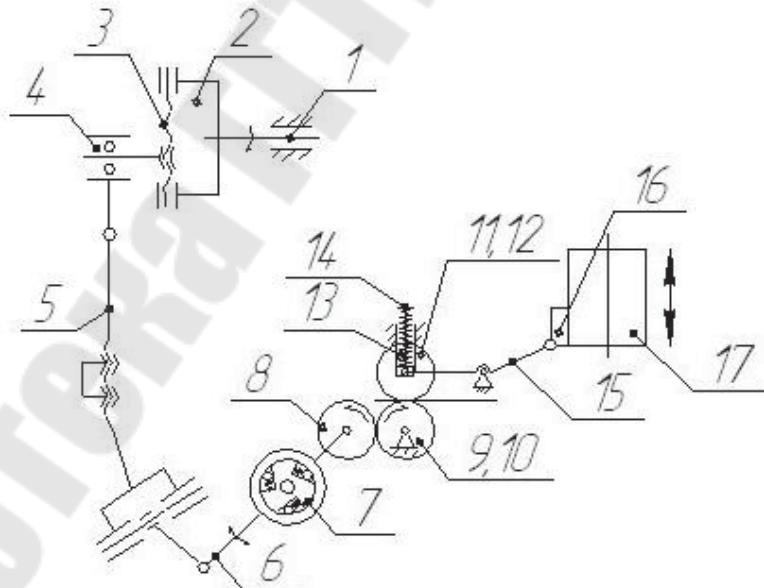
Кинематическая схема привода односторонней толкающей валковой подачи от главного вала: 1 - кривошипный вал; 2 - планшайба; 3 - регулировочный винт; 4 - кривошип; 5 - тяга; 6 - рычаг; 7 - муфта обгона; 8, 9, 11 - зубчатые шестерни; 12, 10 - верхний и нижний подающие валки; 13-пружины; 14 - винт; 15 - рычаг; 16 - кулачок, 17 - ползун пресса.
